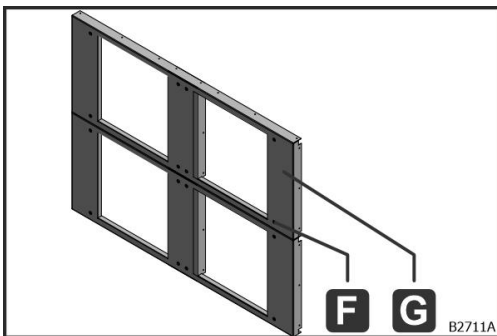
F – Écrou à riveter M8, hexagonal, V2A ; G – Barrière filtrante
